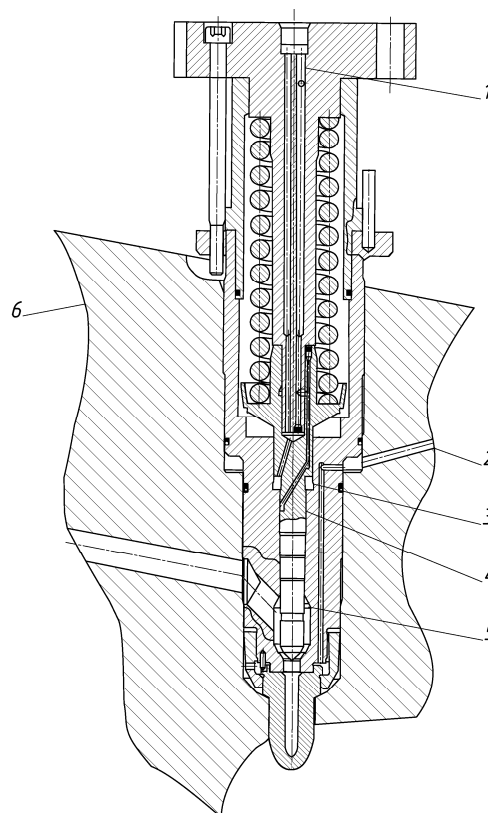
Газова форсунка двигунів ME-GI: 1 – канал підведення керуючого масла; 2 – вентиляційний канал; 3 – порожнина гідравлічного управління голчастим клапаном; 4 – голчастий клапан; 5 – газова порожнина; 6 – кришка циліндра
